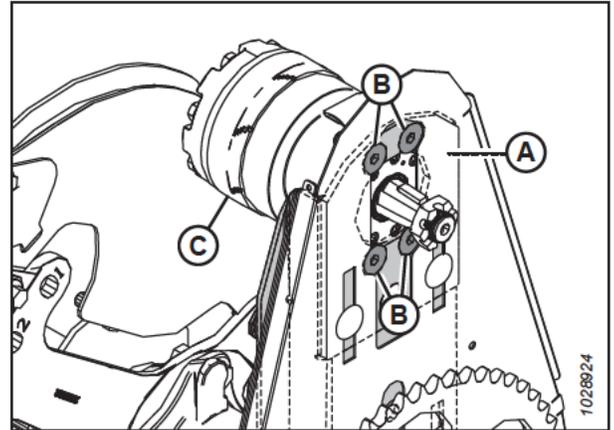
Parafusos de montagem do motor de acionamento do molinete
